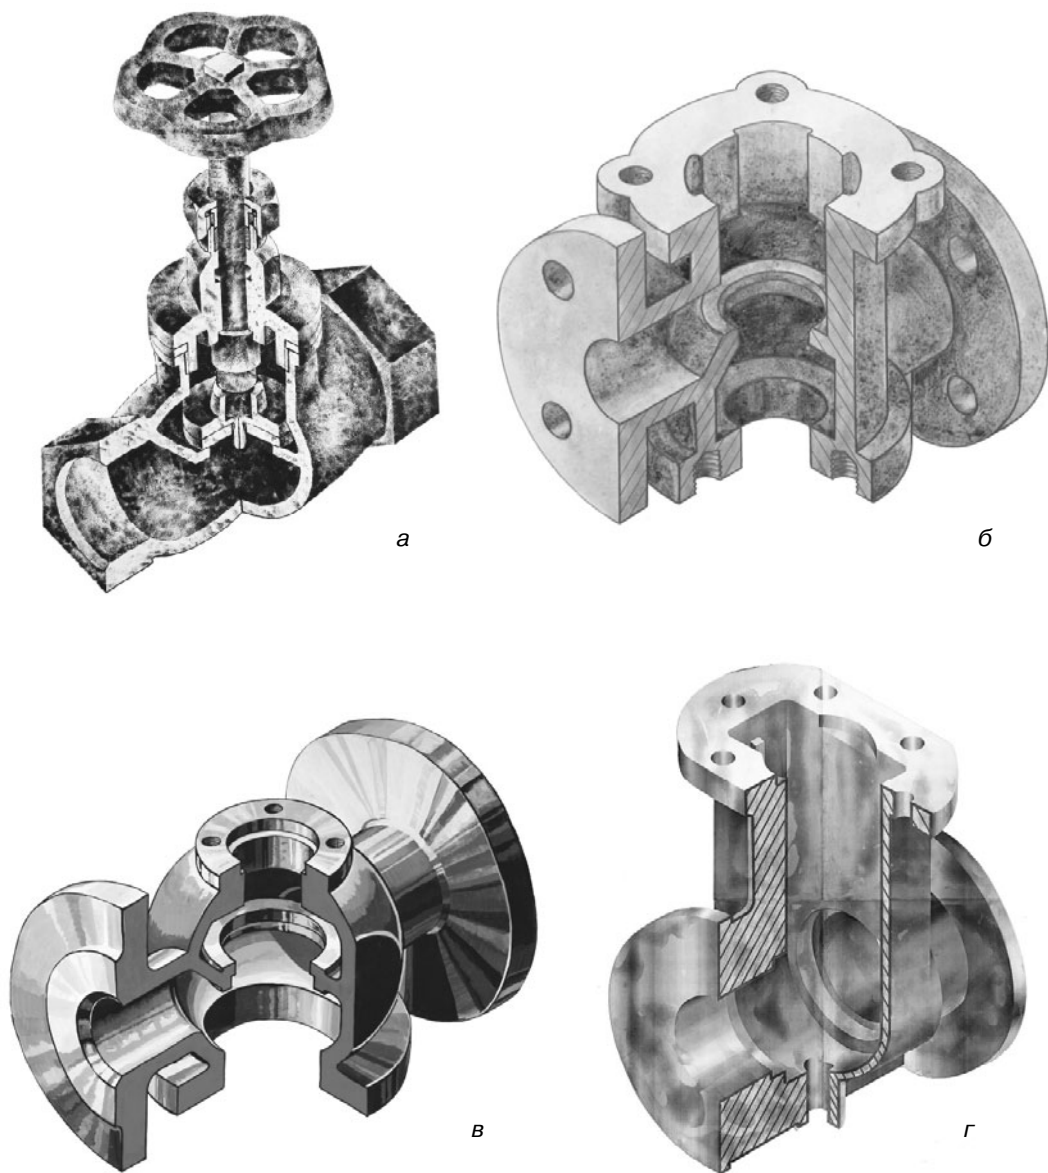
а) тамповка. Устройство вентиля; б) акварель. Корпус вентиля; в) гуашь. Корпус вентиля; г) аппликация. Корпус задвижки (см. цв. вкл.)
